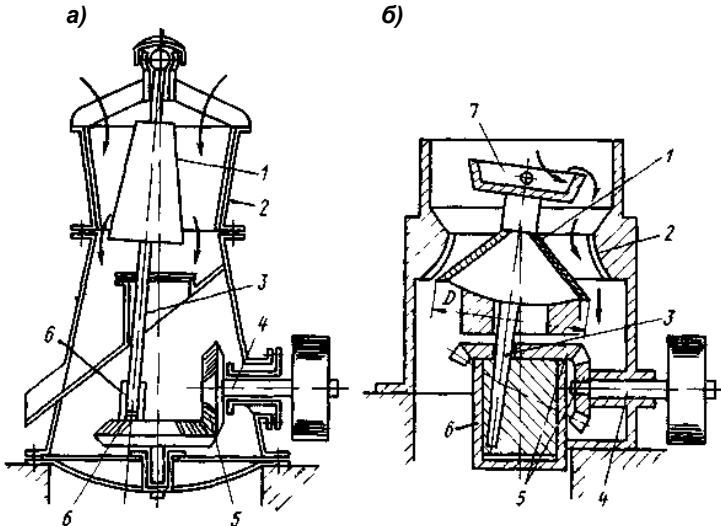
Схема работы и устройство конусных дробилок: а - с подвесным валом (ККД); б - с консольным валом, опирающимся на шаровой подшипник (КСД и КМД): 1 - подвижный дробящий конус; 2 - неподвижный конус; 3 - вал дробилки; 4 - приводной вал; 5 - зубчатая пара; 6 - эксцентриковый стакан; 7 - распределительная тарелка
